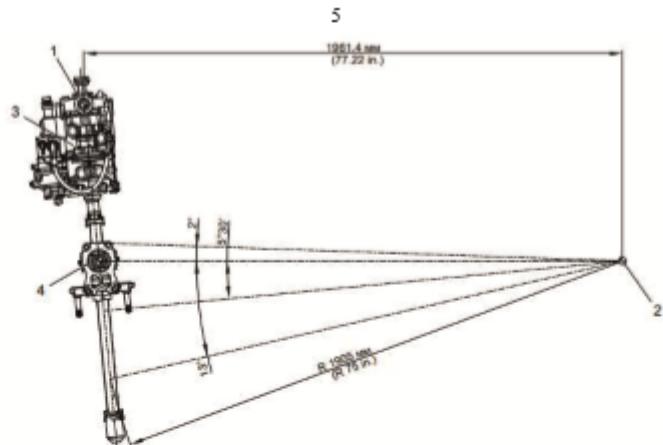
Кинематическая схема механизма перестановки стабилизатора
